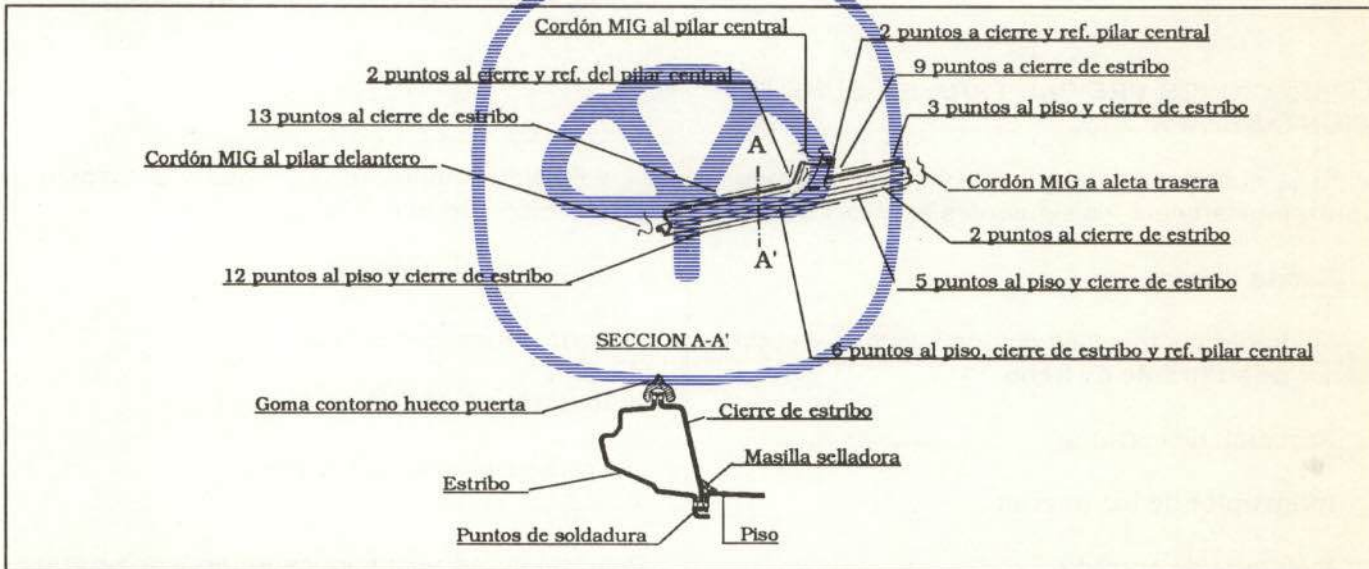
UNION DEL ESTRIBO CON CARROCERIA
